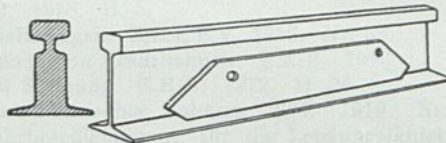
Im Lichtbogen geschweißte Stoßverbindung.
